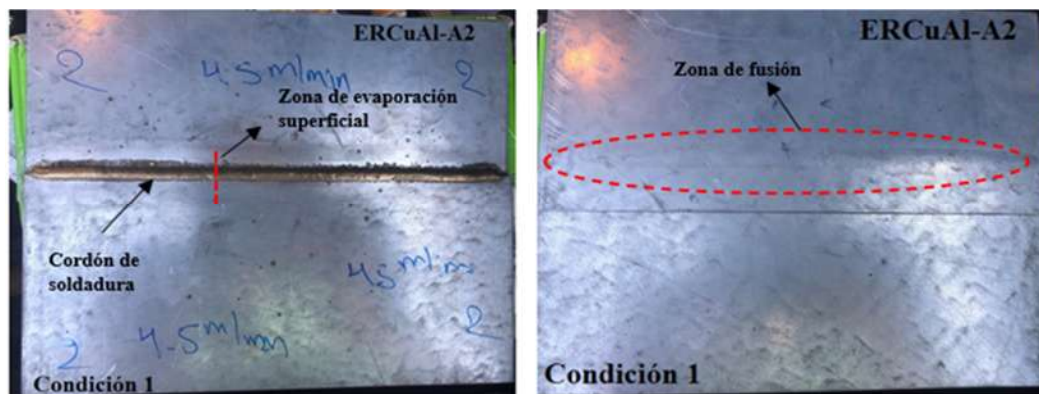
Unión soldadas con el electrodo ERCuAl-A2 mediante el proceso GMAW-P Brazing. C1-B.
